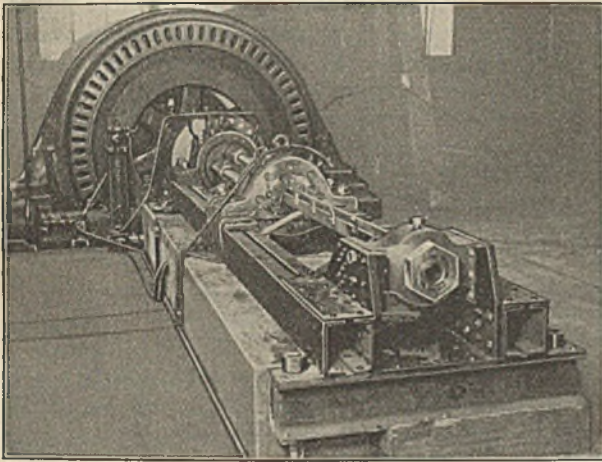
Streckwalzwerksanlage, Bauart Kocks.
